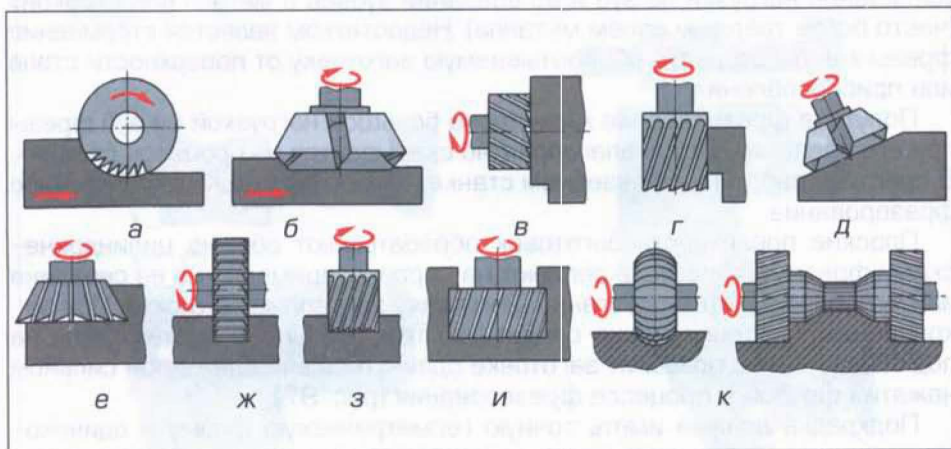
Разновидности операций фрезерования:  $a$  – цилиндрическими фрезами на оправке,  $б$  – торцевыми фрезами или фрезерными головками,  $в, г$  – торцевыми фрезами на концевой оправке,  $д, е$  – одноугловыми и двухугловыми фрезами,  $ж, з, и$  – дисковыми трёхсторонними и концевыми фрезами,  $к$  – фасонными фрезами и набором фрез
